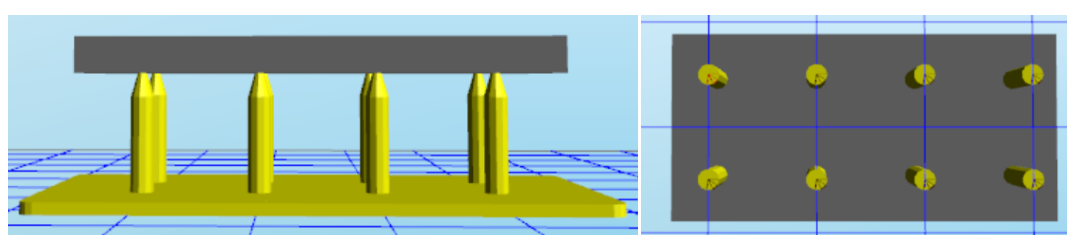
Vista frontal y desde abajo del CAD de la pieza probeta 4.
